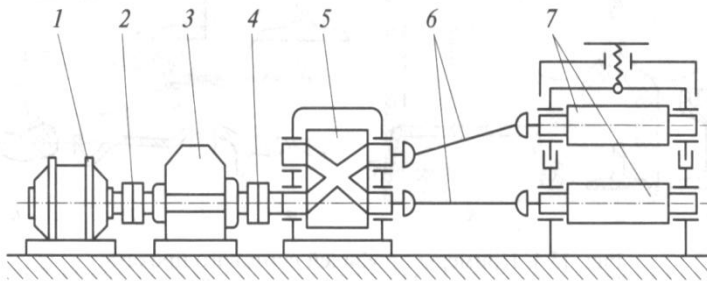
Схема прокатного стана: 1 — электродвигатель; 2 — упругая муфта; 3 — редуктор; 4 — главная (трефовая) муфта; 5 — шестеренная клетка; 6 — шпиндели; 7 — рабочие валки
